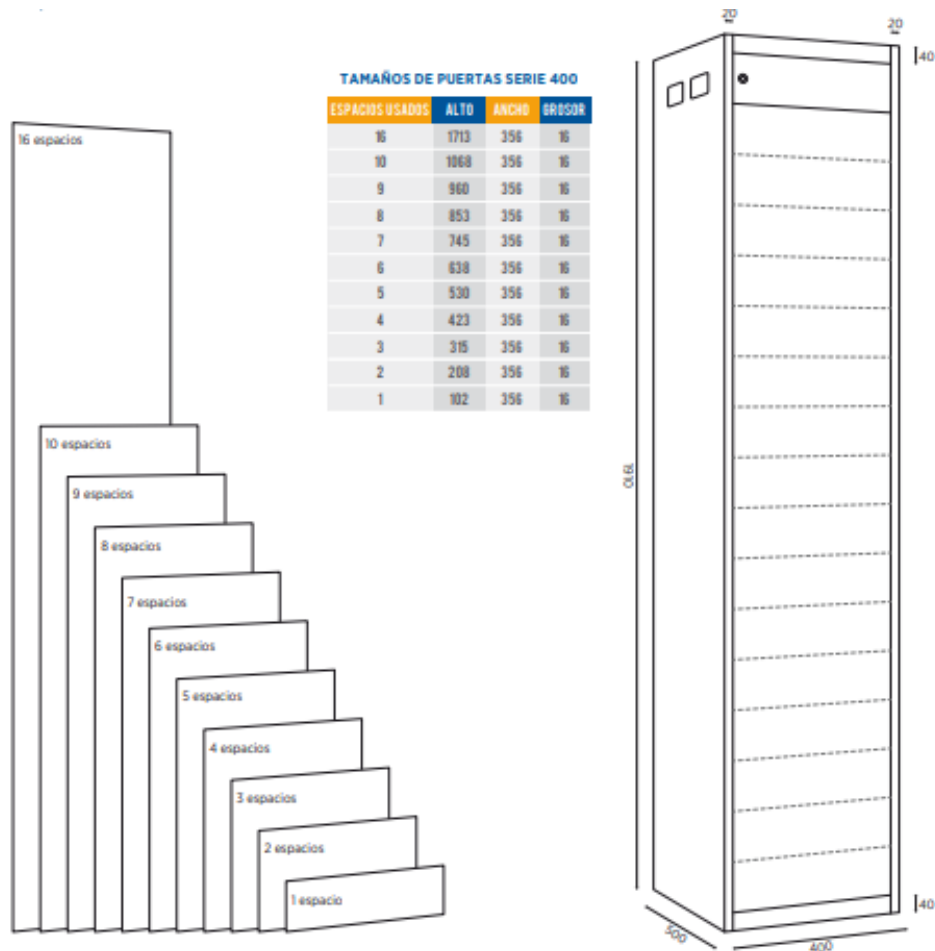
Explicación de la estructura combinable de una SmartLocker de Setronic - <http://www.setronic.com>
